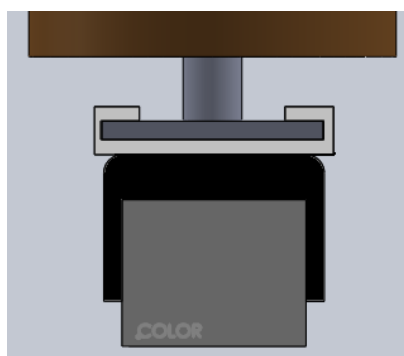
Carimbo acoplado ao êmbolo do cilindro.
